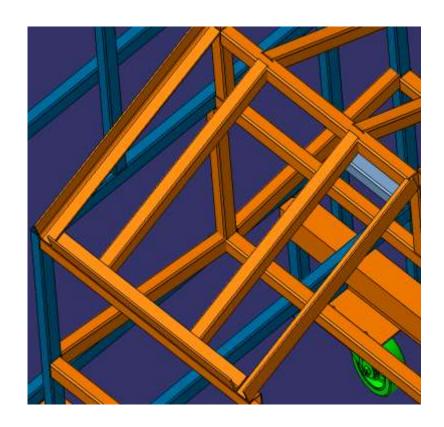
D модель конструкции под углом для крепления и удержания пластиковой коробки под углом
